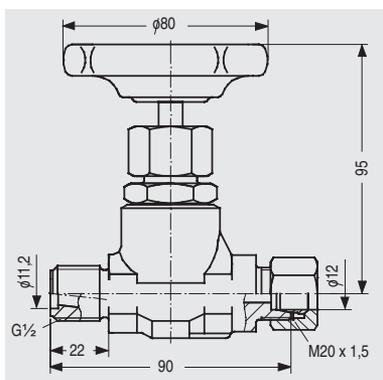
/133 Запорный вентиль 7MF9017-1B, -2B, -3B, размеры
